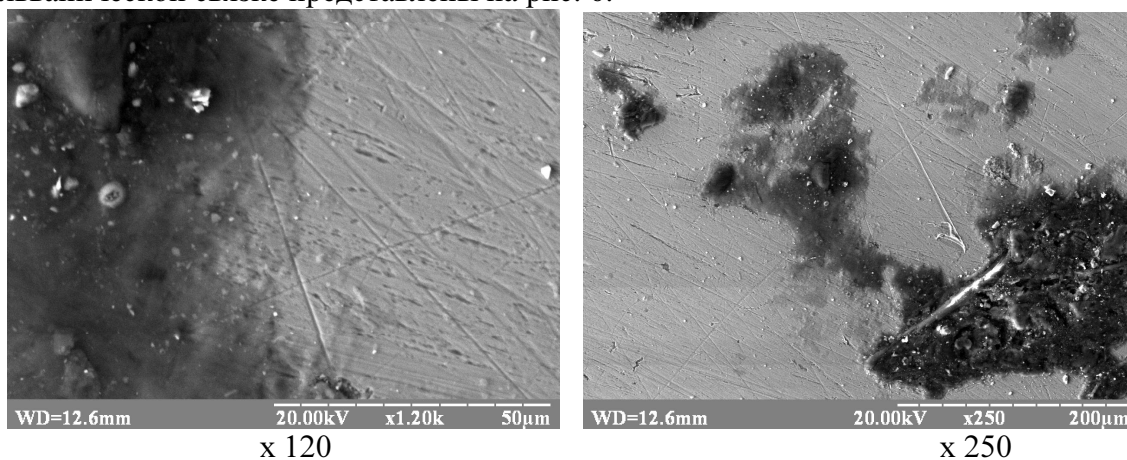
Поверхность образцов магнитов из сплава ЮН15ДК25БА после обработки кругами на гальванической связке на станке HSG – TECHNOLOGIE
